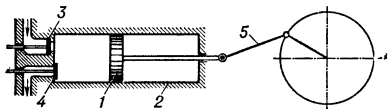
Схема поршневого детандера: 1—поршень; 2—цилиндр; 3—впускной клапан; 4—выпускной клапан; 5—кривошатунный механизм.
